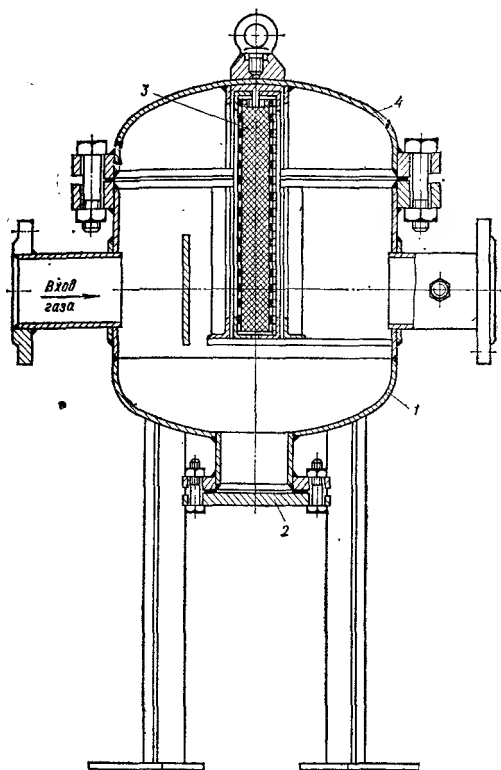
Волосяные стальные сварные фильтры
